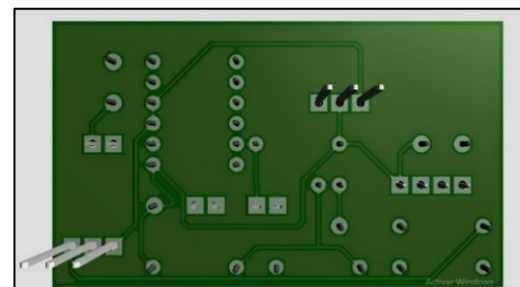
Modelado en 3D de la PCB vista inferior. Fuente: Propia
